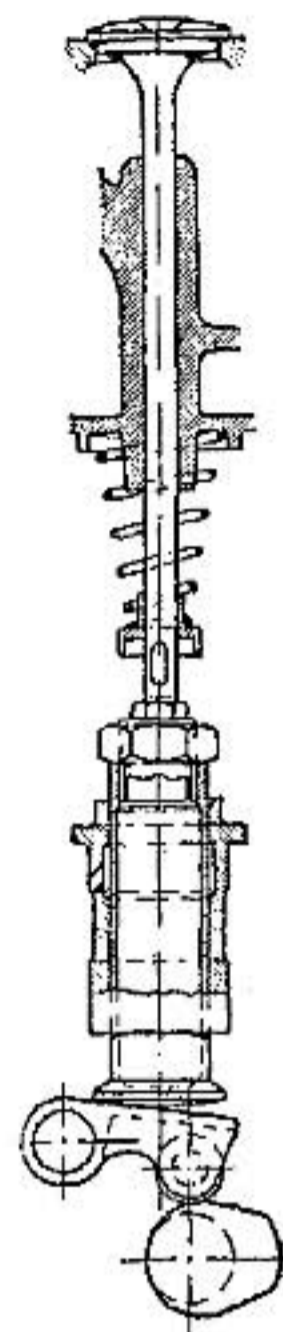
Двух-затворный клапанъ двигателя Адлеръ.
